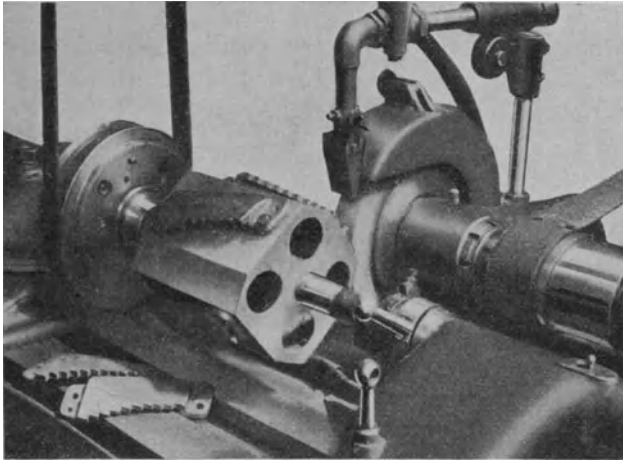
Schleifen von Segmentstücken auf einer Vorrichtung.
